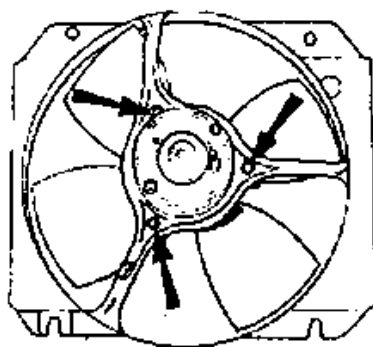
Porcas de fixação do motor do ventilador ao defletor de ar do radiador.
